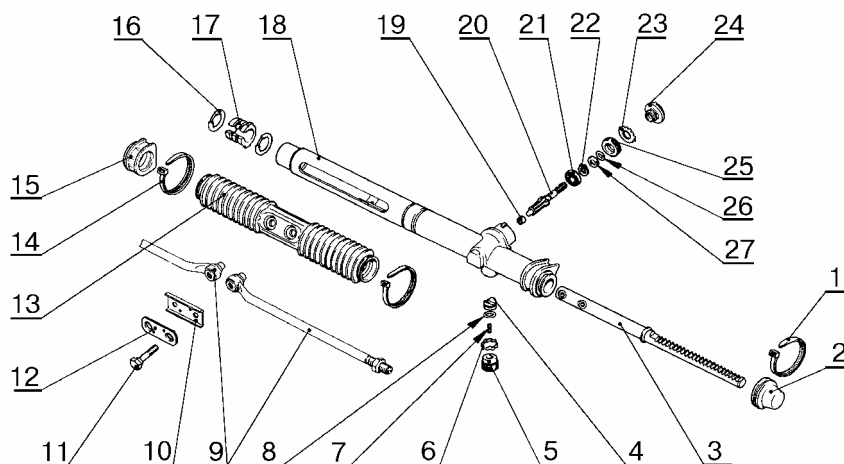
Детали рулевых механизмов 2108-3400012-10, 2110-3400012-20:
